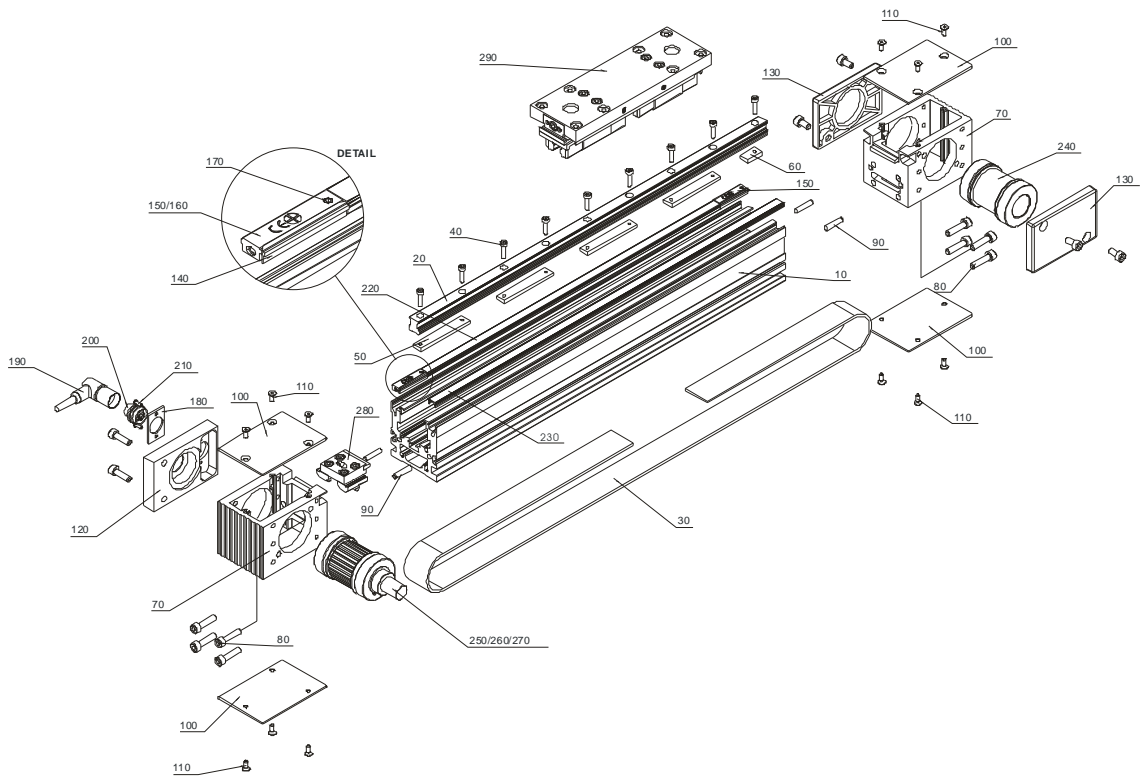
Modul 65/15, Explosionszeichnung, Teilegruppen-Nr.: 1001028
